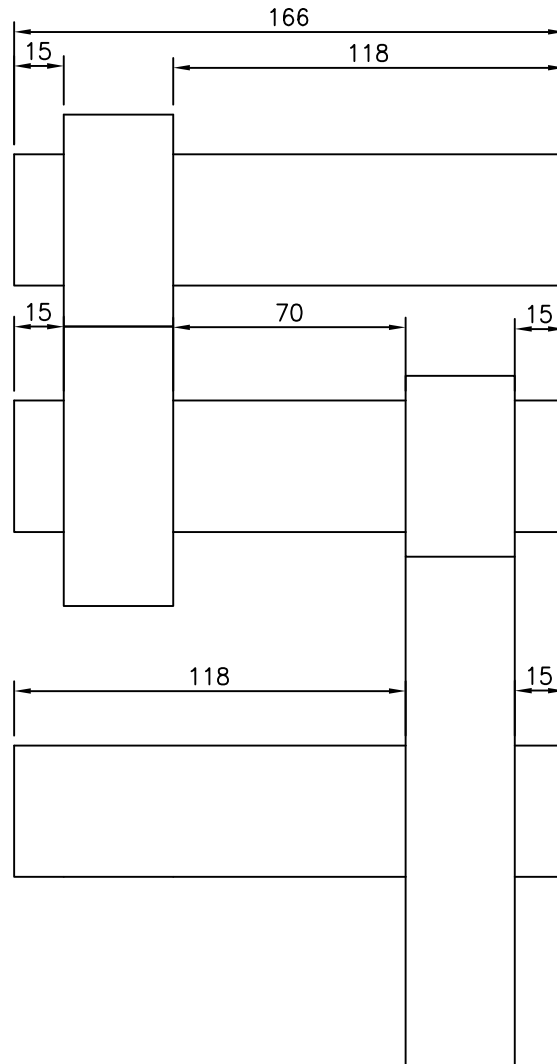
Esquema cinemático do conjunto de engrenagens. Fonte: elaborada pelo autor
